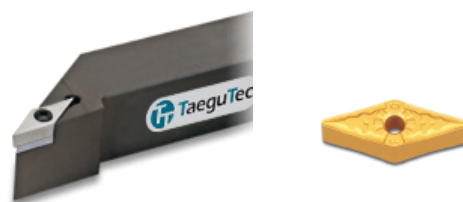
Сборный токарный резец с углом в планк 93° и со сменной многогранной пластиной TT8115
